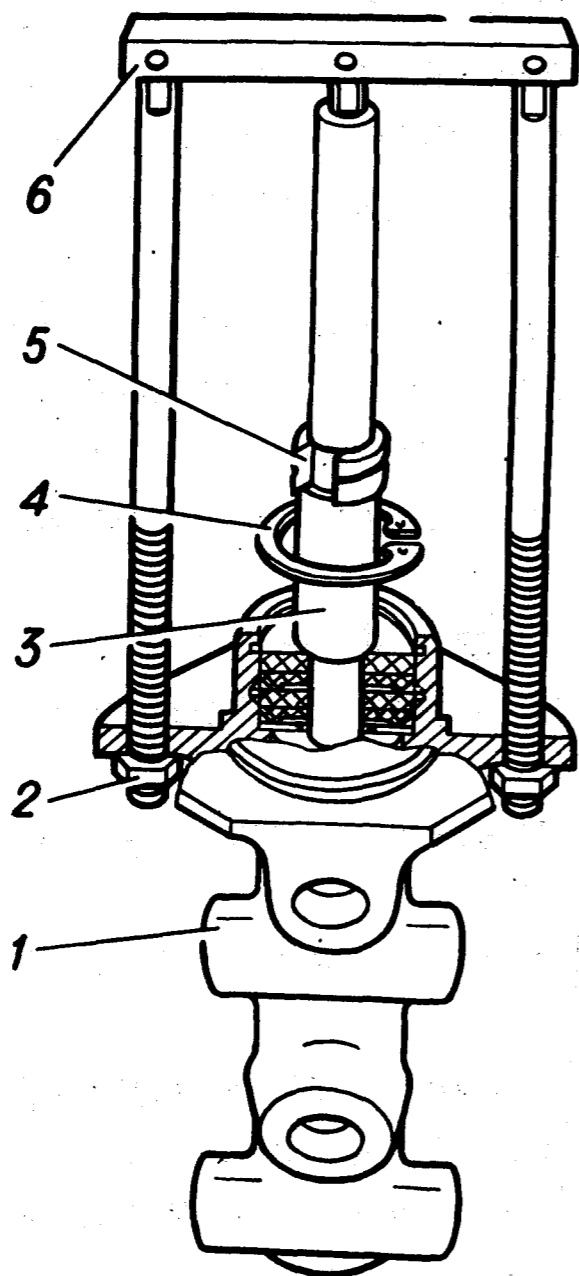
Приспособление 6999-7566 для сборки главного цилиндра:
